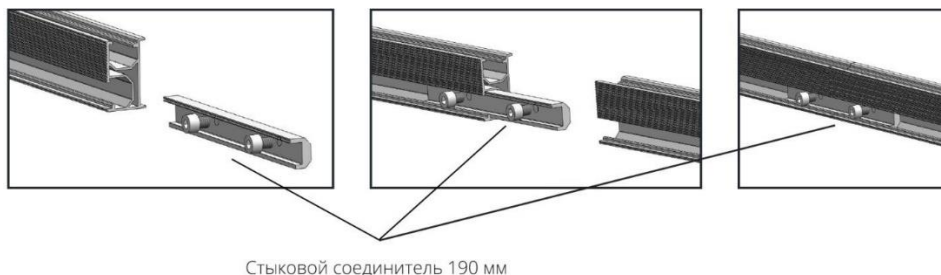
Соединение двух и более профилей с помощью стыкового соединителя.
